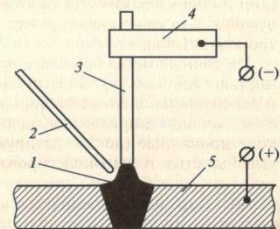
Схема сварки неплавящимся электродом:
